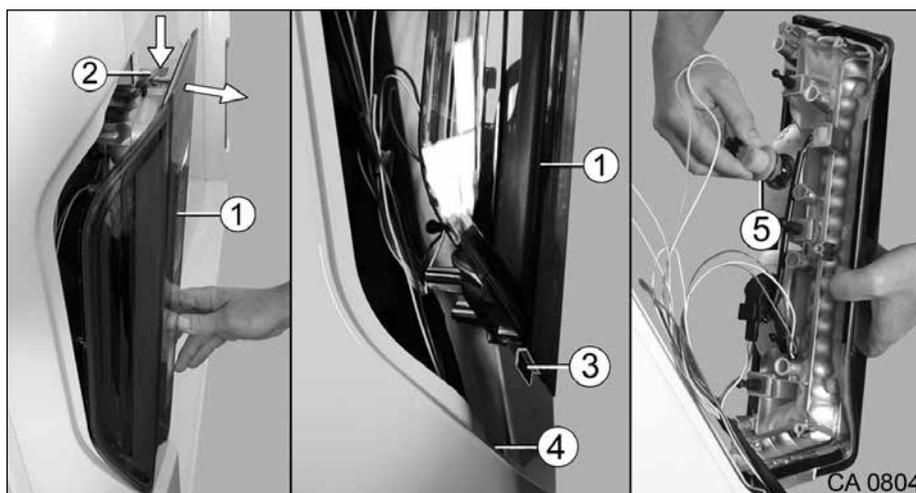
Remplacement de l'ampoule sur le support de feu arrière
